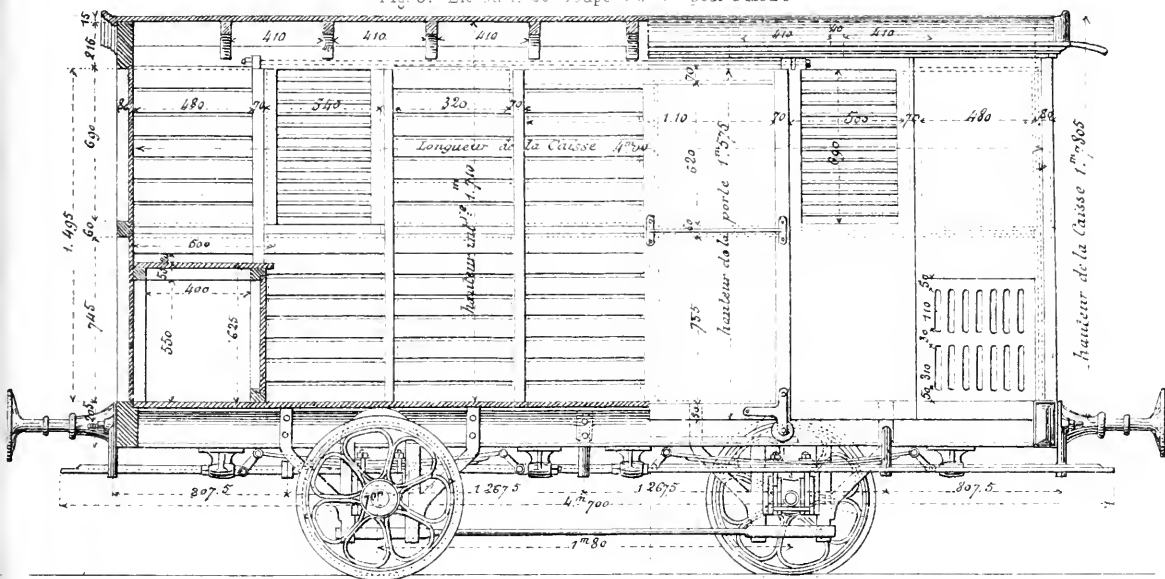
Demi-plan, Coupe de la Caisse à 0^m03 pour 1 Mètre.
